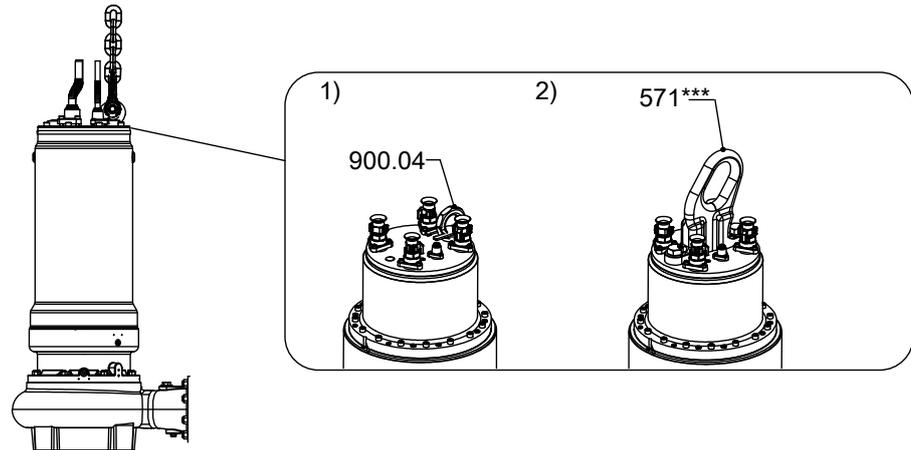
Colocación de la cadena/cuerda de izado - Instalación en zona seca
